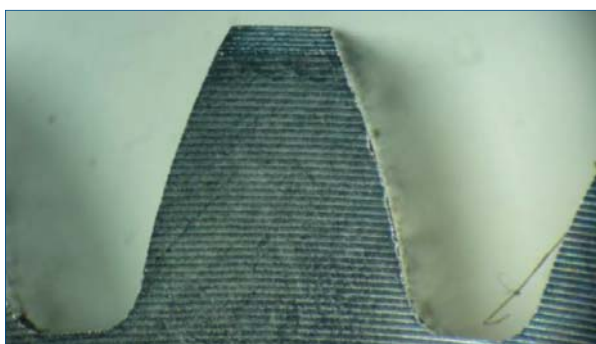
Боковые поверхности зубьев до чистовой обработки
